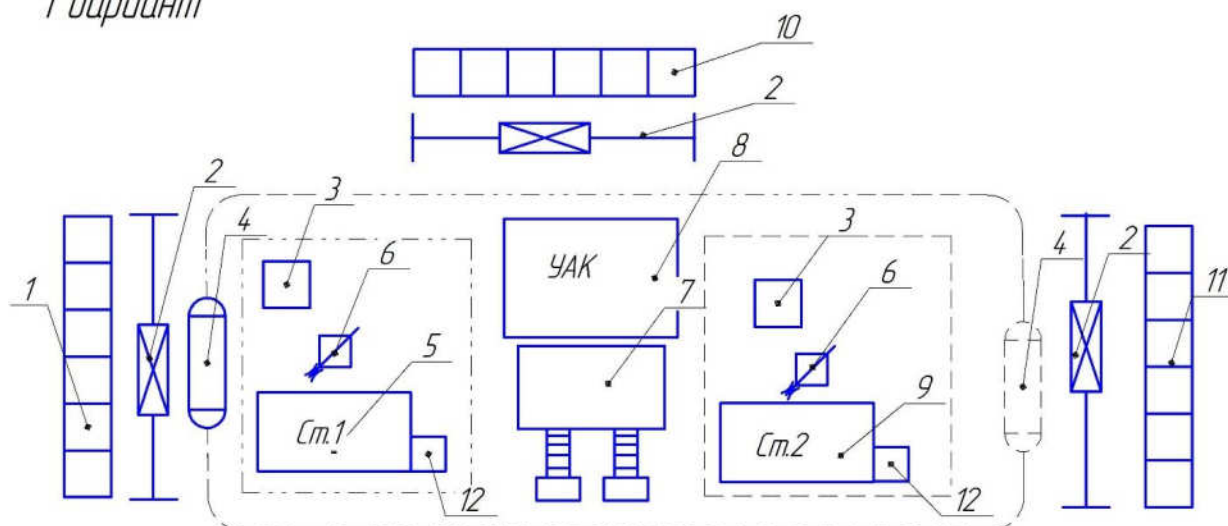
Первый вариант расположения оборудования (1-склад заготовок; 2-кран-штабелер; 3-приемо-раздаточный стол; 4-робокар; 5-первый обрабатывающий центр с ЧПУ; 6-промышленный робот; 7-моечная машина; 8-участок автоматизированного контроля; 9-второй обрабатывающий центр с ЧПУ; 10-промежуточный склад хранения; 11-склад готовой продукции; 12-тара для стружки)
